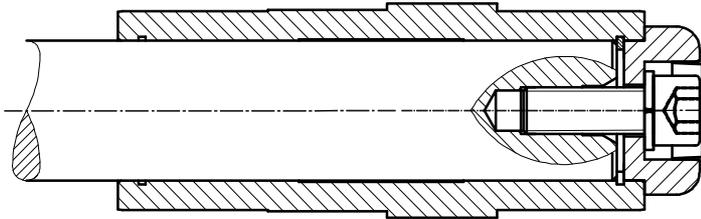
Крепление редуктора к валу без упора с помощью крепежного элемента
